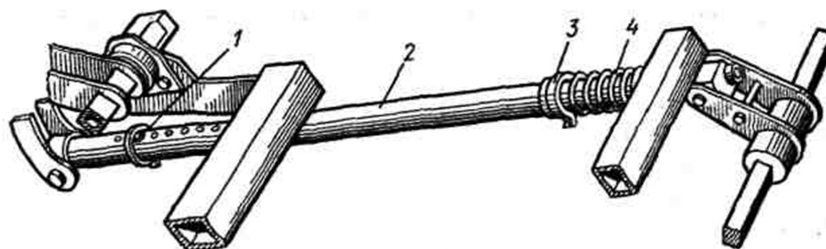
Регулювання глибини ходу загортачів:
